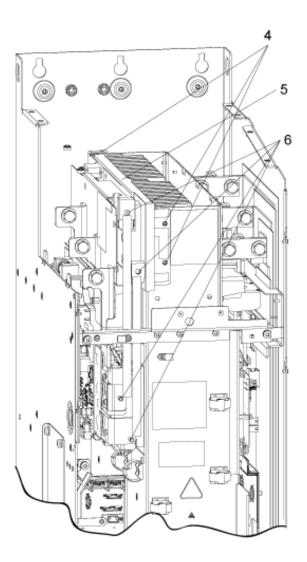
Montaje del Braking Module en un Power Module de tamaño GX: pasos 4 - 6
